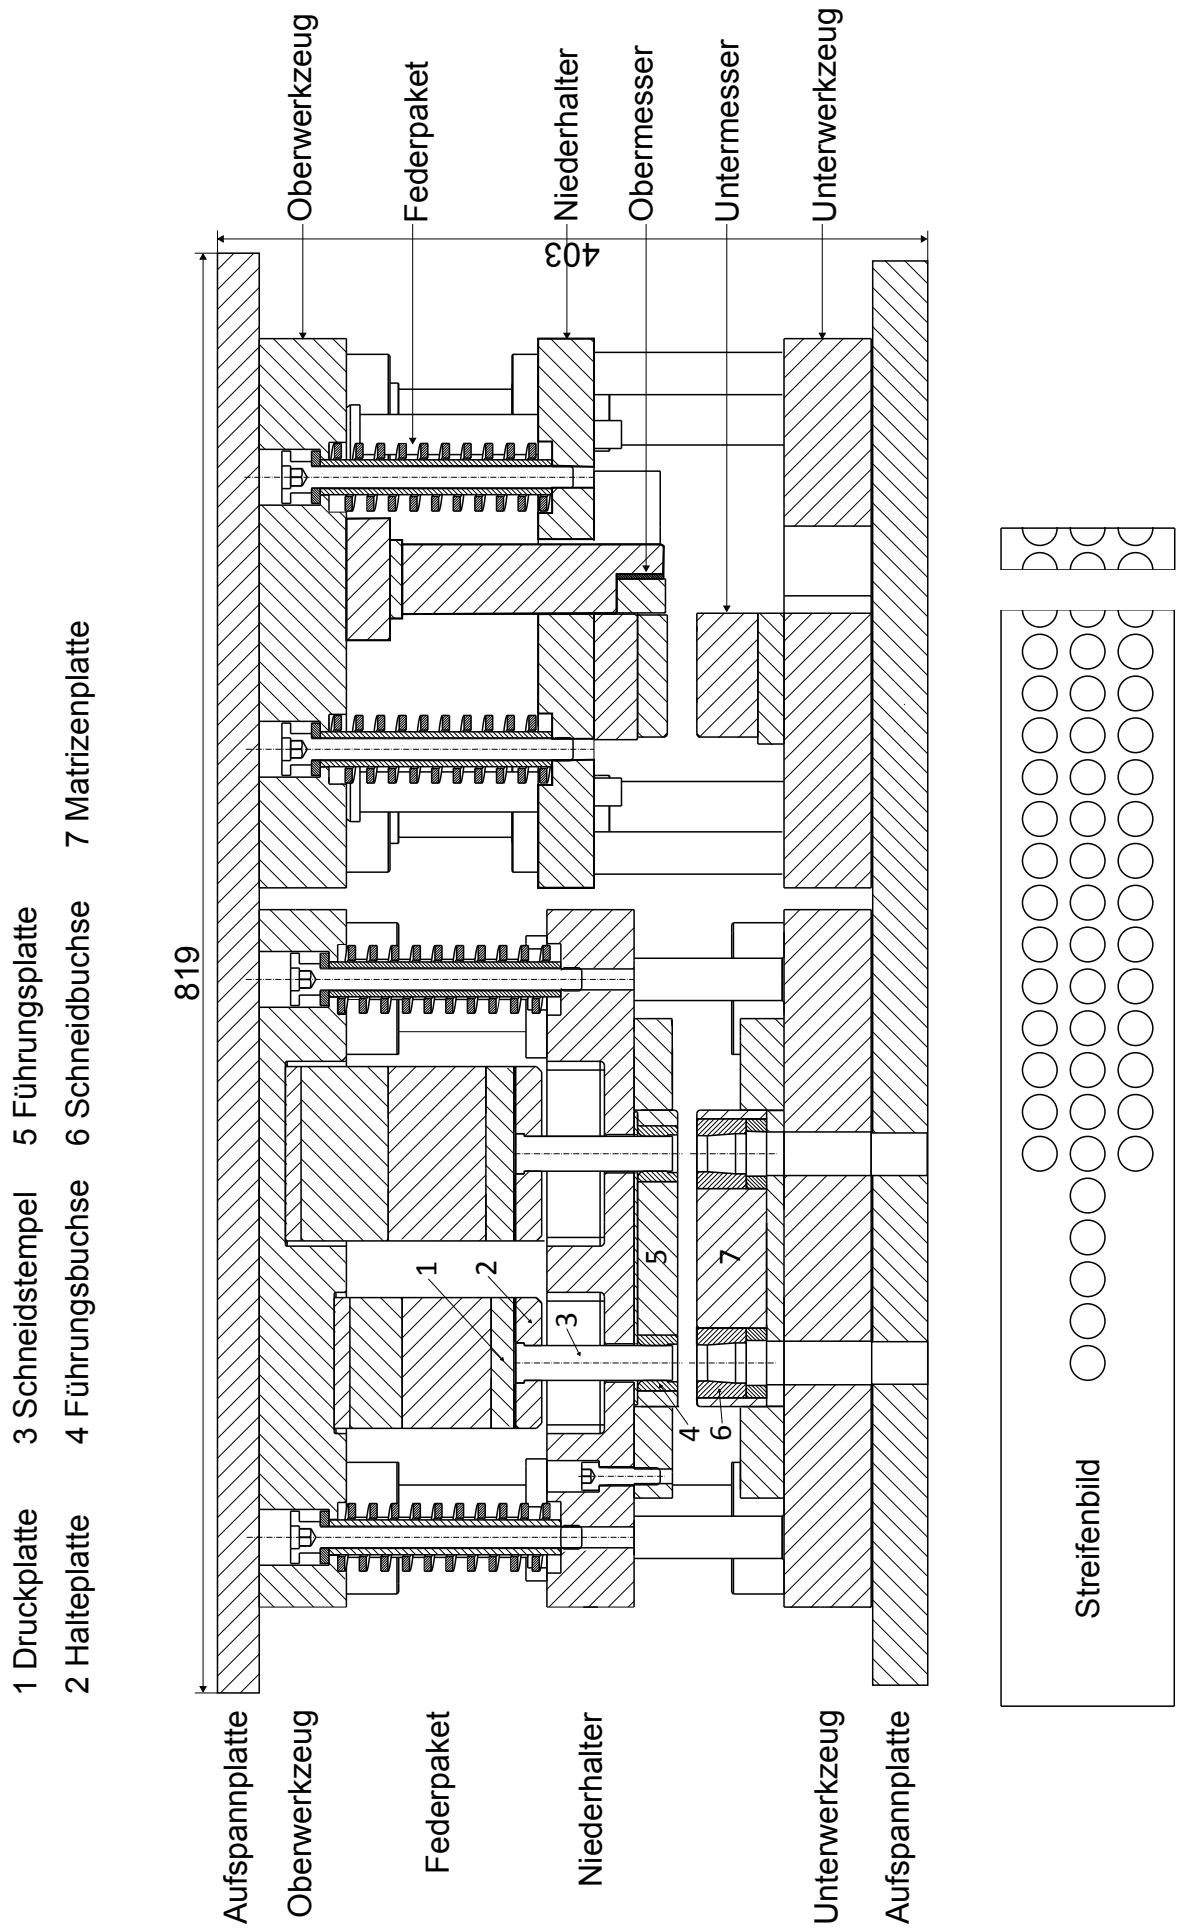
Querschnitt des Dauerhubwerkzeugs
